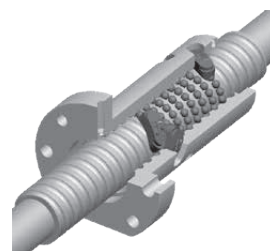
Kugelgewindemutter mit interner Einzelrückführung
